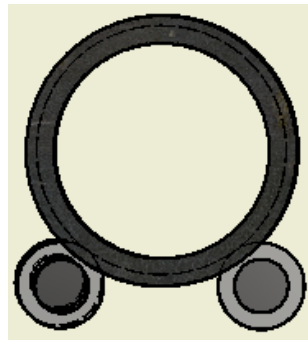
Apoyo del molde en 6 rodets acoplados a 2 ejes.
